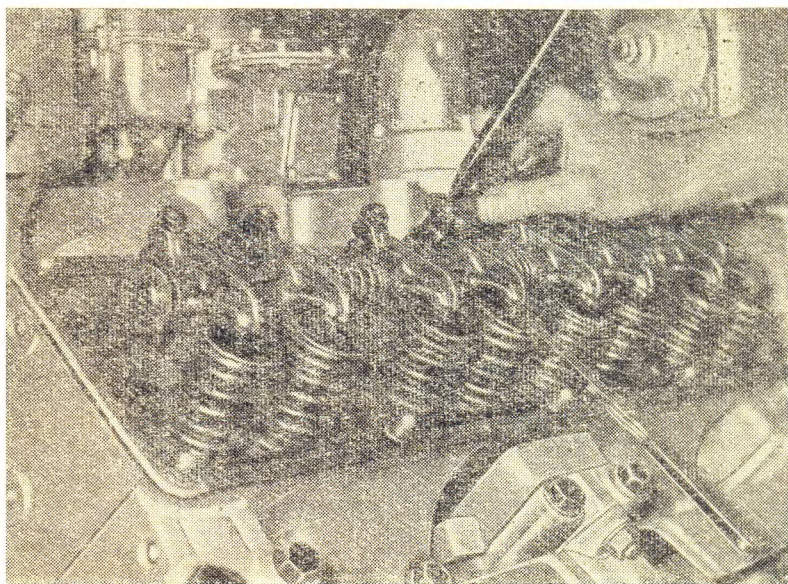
Измерение зазора между клапаном и коромыслом и его регулировка
